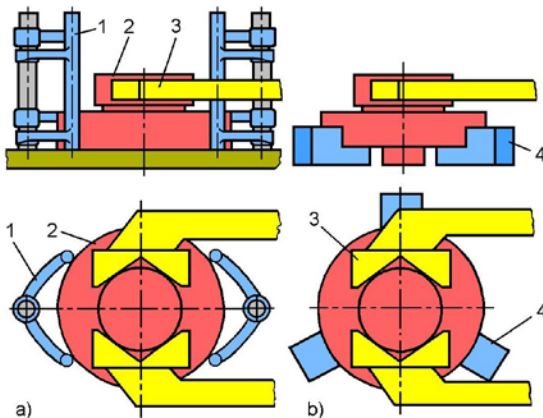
Zugänglichkeit für den Werkstückgreifer zum Magazinplatz (Durchmesser einstellbar). a) Vierpunktaufnahme mit Stapelbildung, b) Dreipunktaufnahme für Einzelwerkstücke, 1 Schachtmagazin-Element, 2 Werkstück, 3 Greifbacke, 4 Werkstückaufnahme-Element
